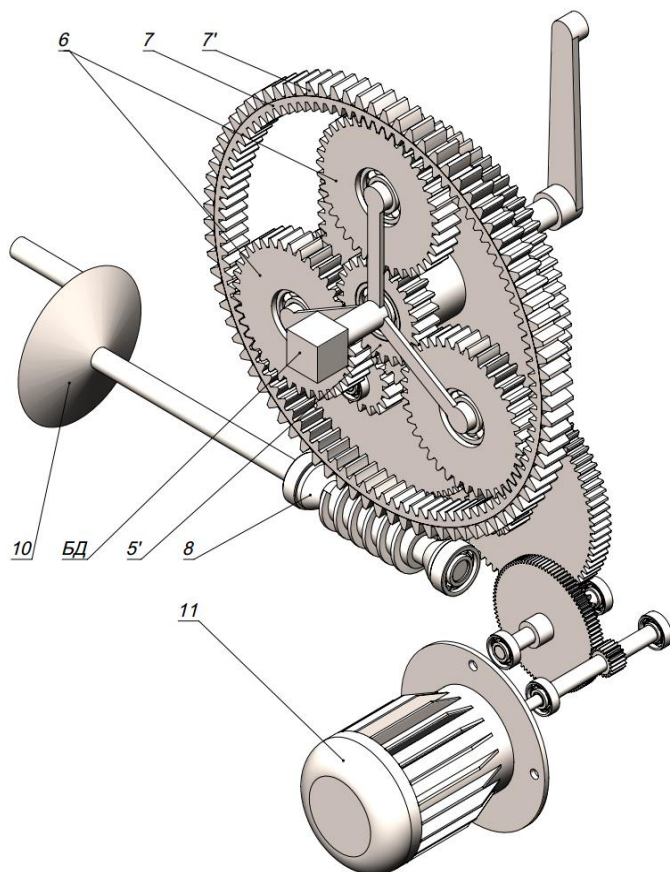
Кинематическая схема редуктора ИОМ:
